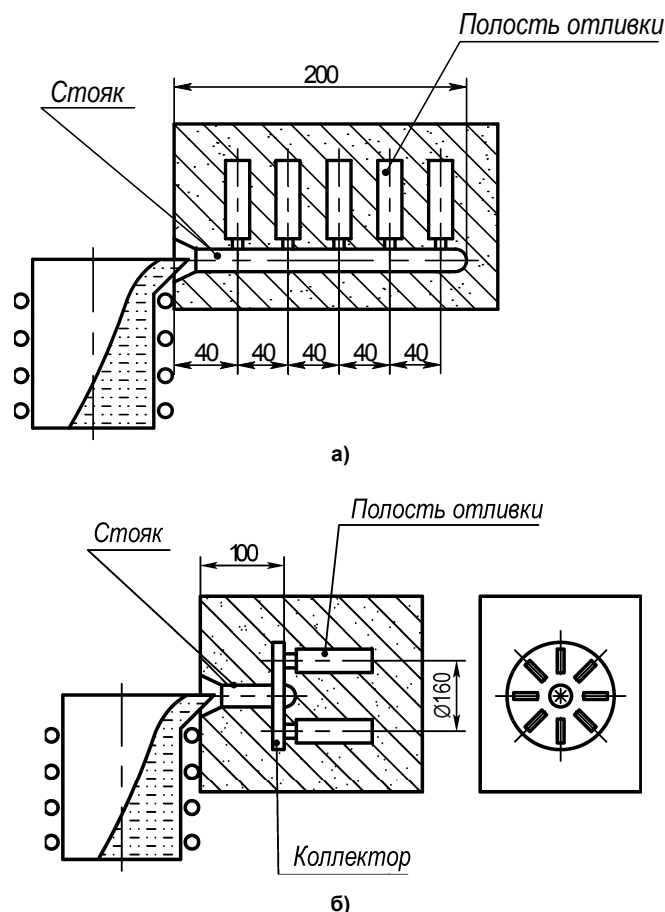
Расположение отливок в форме: а – схема I; б – схема II
